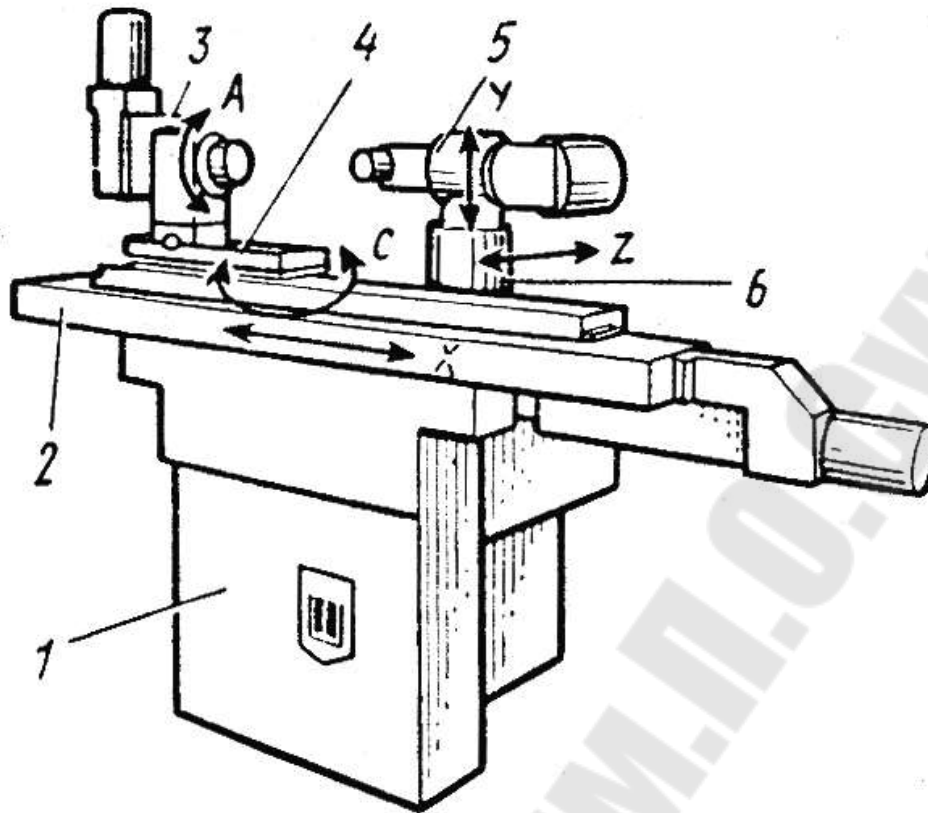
Общий вид многоцелевого заточного 5-координатного станка с ЧПУ: 1 – станина; 2 – стол; 3 – бабка изделия; 4 – поворотное основание бабки изделия; 5 – шлифовальная бабка; 6 – колонна
